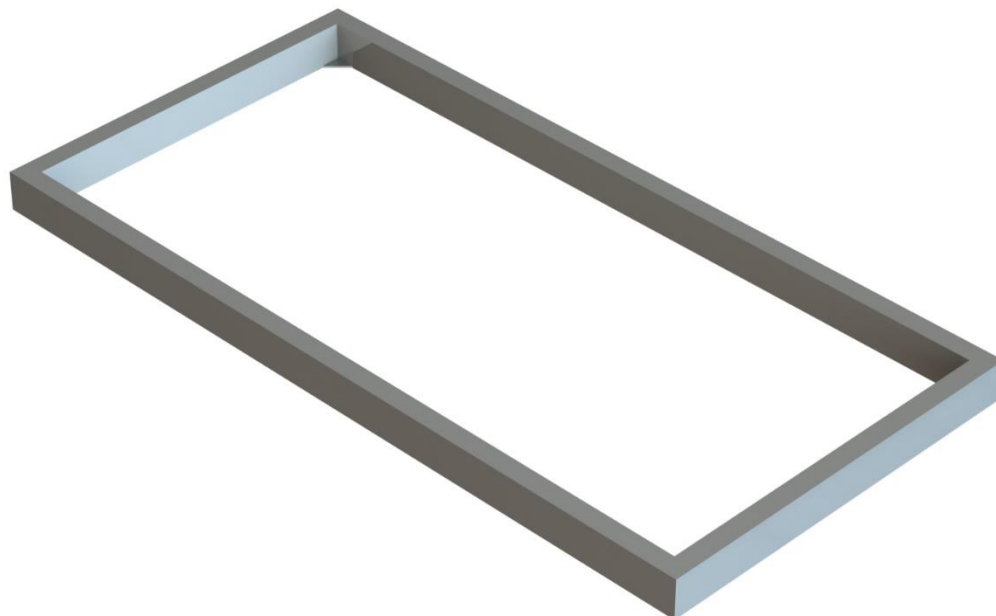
Tubos de aço e cantos de união soldados.
